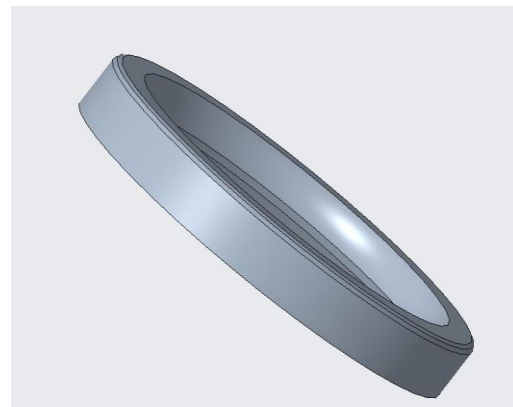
Dodaný model sacího ventilu motoru TATRA T3C 928 [46]
